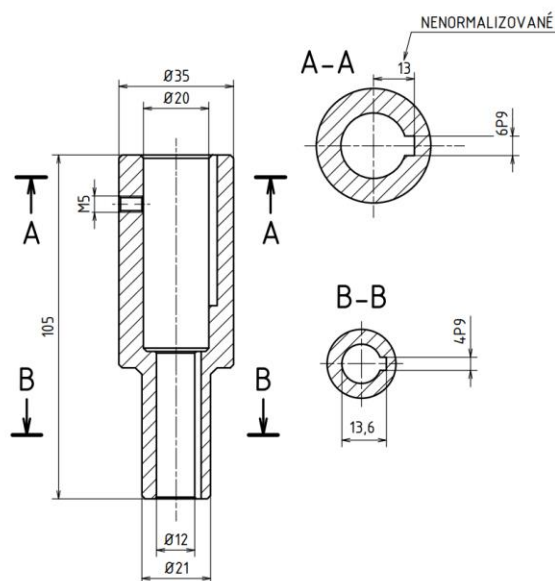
Spojení elektromotoru se skříní a spojkou
